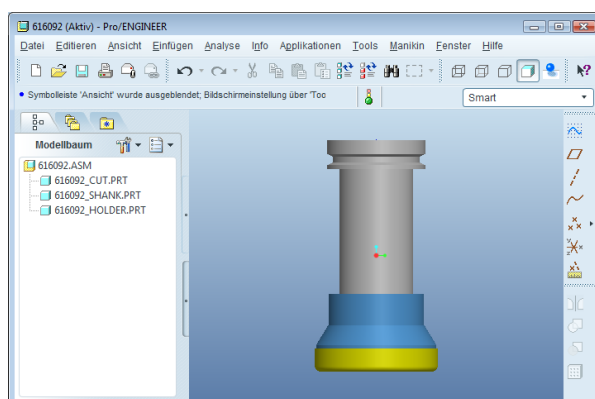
Modellbaum des Komplett-Werkzeuges
